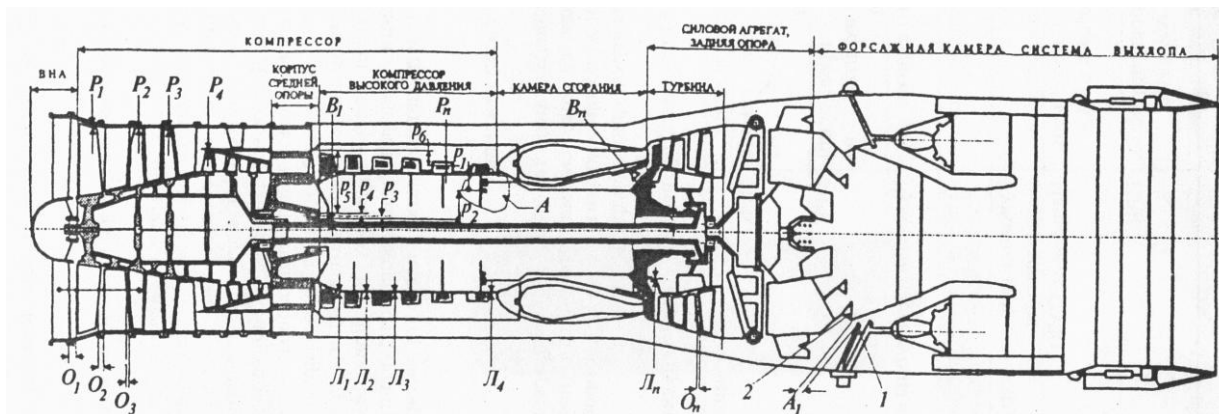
Схема турбореактивного двухконтурного двигателя с форсажной камерой
